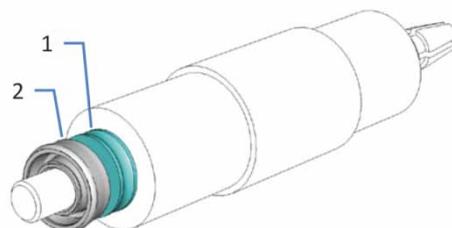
Stützring und Kolbendichtung auf dem Einbaupin für die Dichtung
